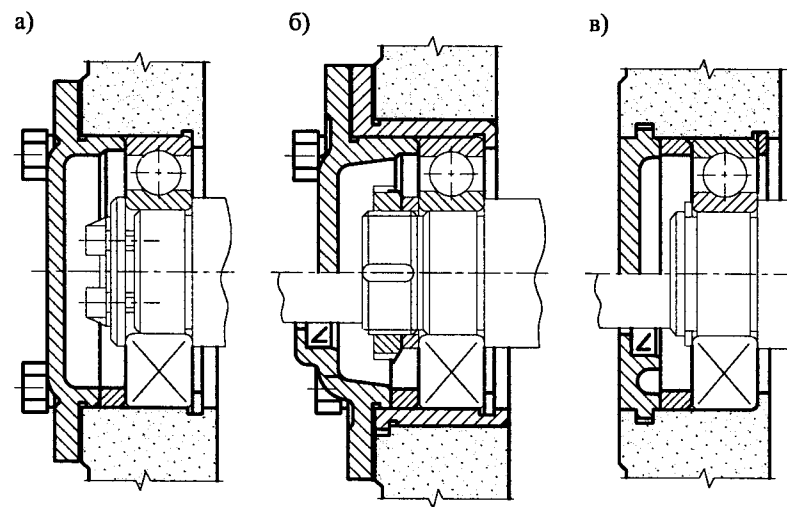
Установка наружного кольца неразъемного подшипника в корпусе фиксирующей опоры
